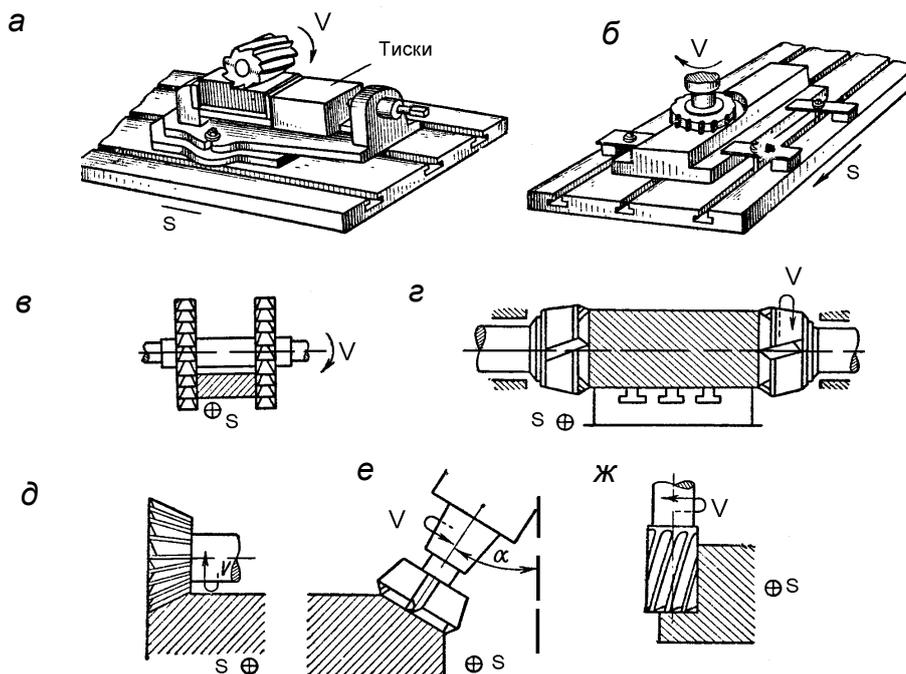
Основные виды фрезерования плоских поверхностей: а – обработка горизонтальных поверхностей в тисках; б – обработка горизонтальных поверхностей с закреплением деталей на столе станка; в – обработка вертикальных поверхностей с применением дисковых трехсторонних фрез; г – обработка вертикальных поверхностей торцовыми фрезами; д – обработка наклонных поверхностей одноугловыми
